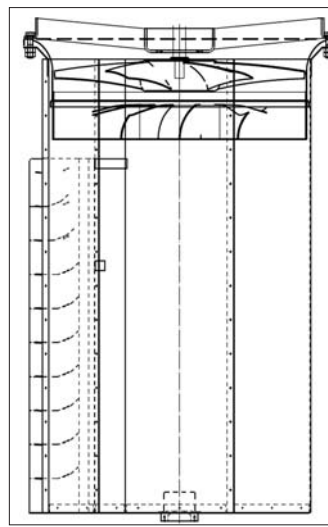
Воздухораспределительный тубус с крыльчаткой и направляющим колесом
